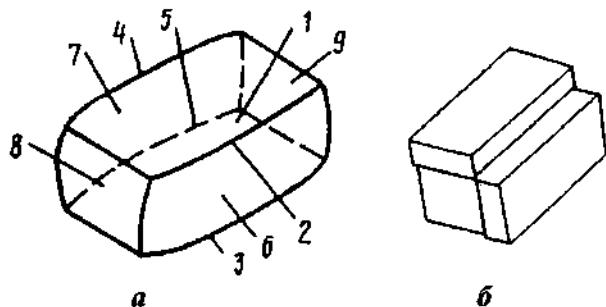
Режущие пластины: а) для резца с клиновым креплением б) Г-образной формы.
